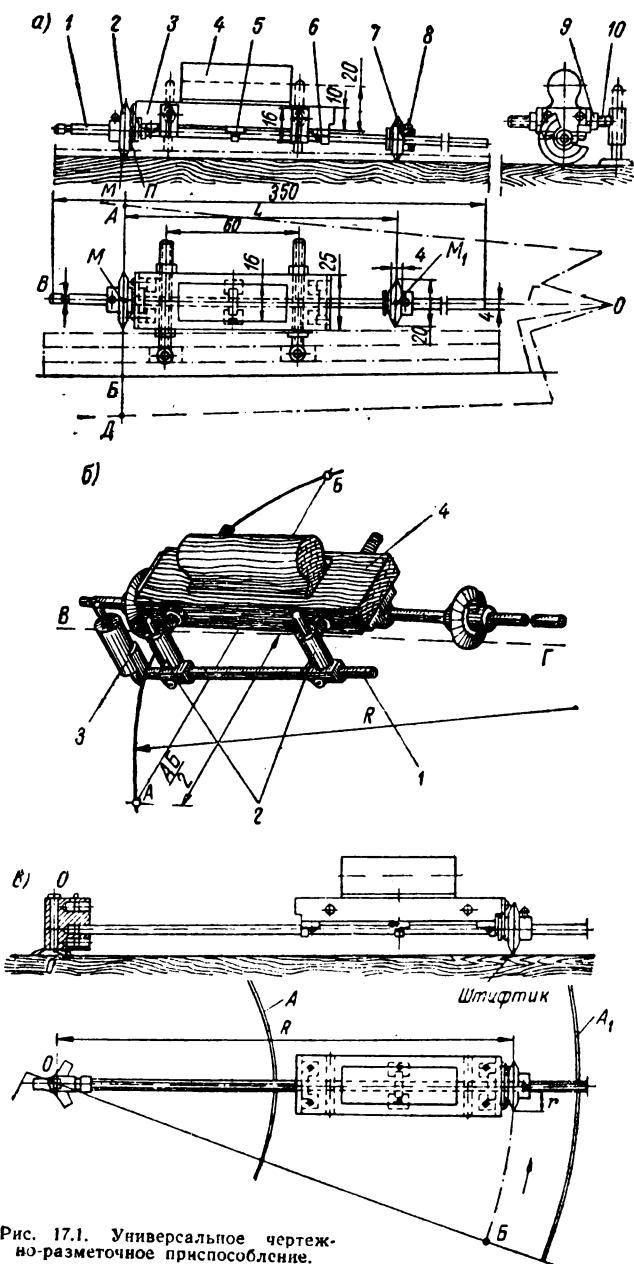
Универсальное чертежно-разметочное приспособление.
